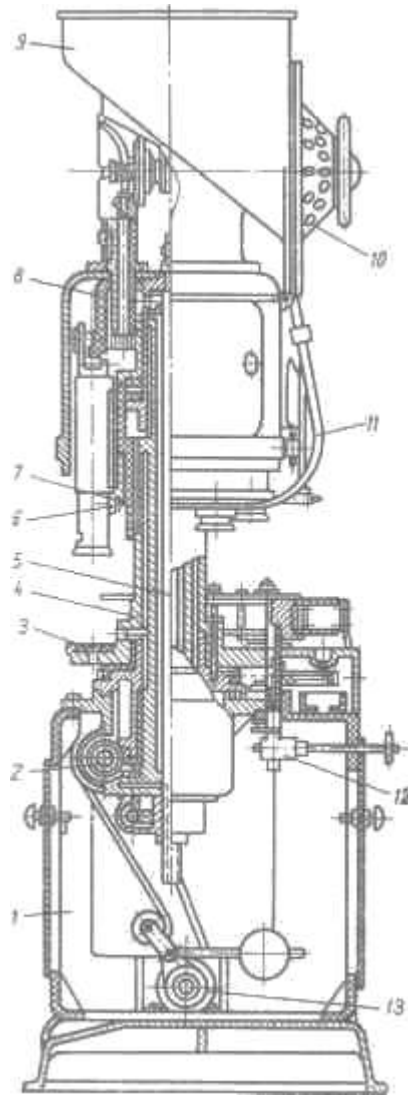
Закупорювальний автомат У6-А: 1-корпус; 2-редуктор; 3-карусель; 4-колонка; 5-стержень; 6-корпус закупорювальних патронів; 7-закупорювальний патрон; 8-копір; 9-бункер; 10-диск для орієнтації; 11-лоток; 12-пневматичний останов; 13-ведучий вал.
